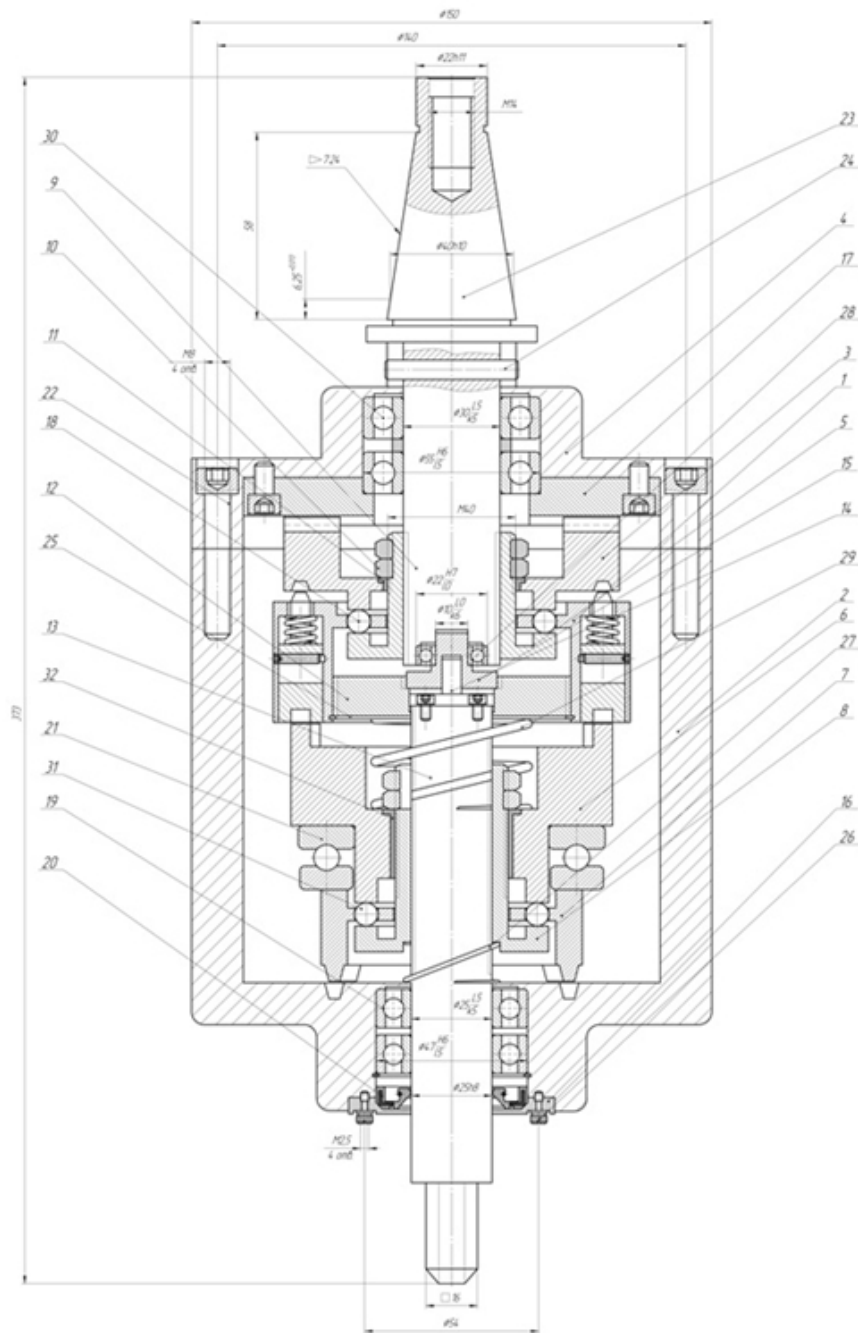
Резьбонарезной патрон на основе передачи с промежуточными телами качения с автоматическим реверсом
